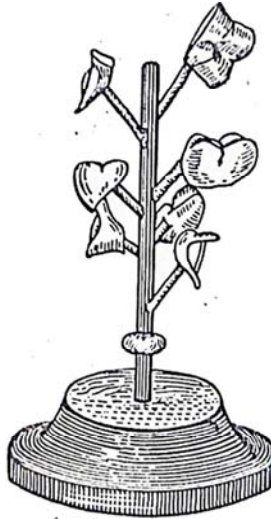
Установка литникообразующих штифтов при одновременной отливке большого количества заготовок
